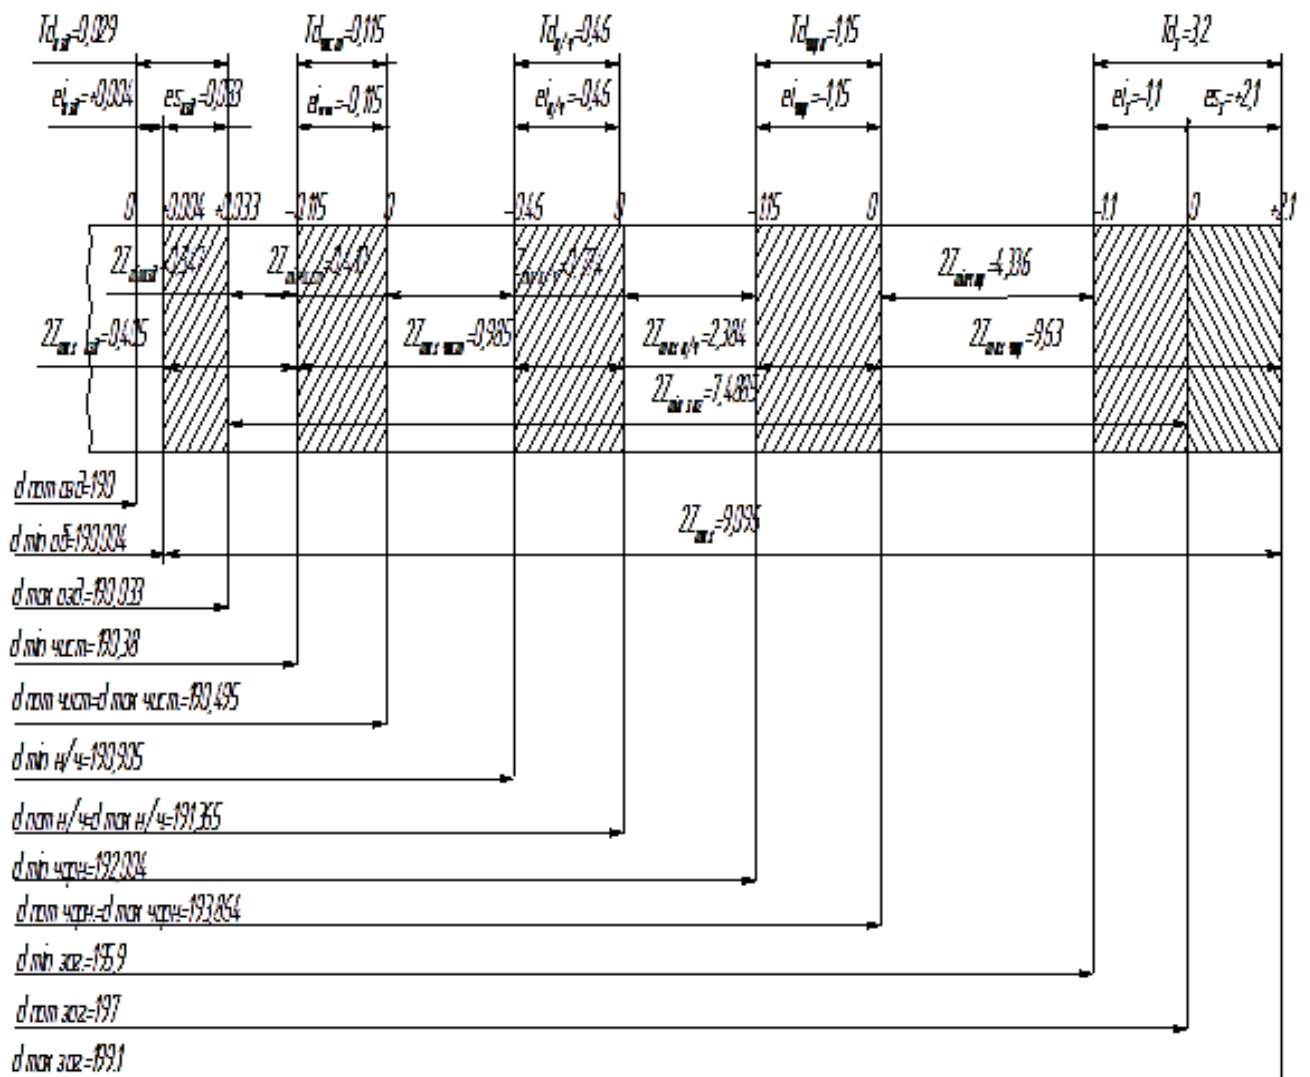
Схема припусків та допусків оброблення зовнішньої циліндричної поверхні на розмір  $\varnothing 190k6$
